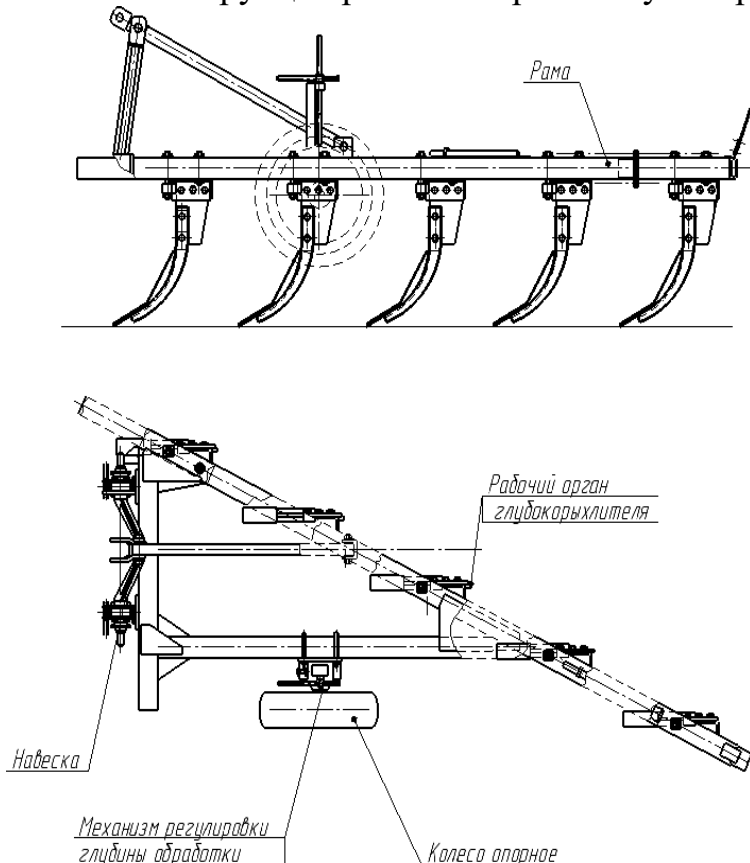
Общий вид глубокорыхлителя на базе правооборотного плуга
